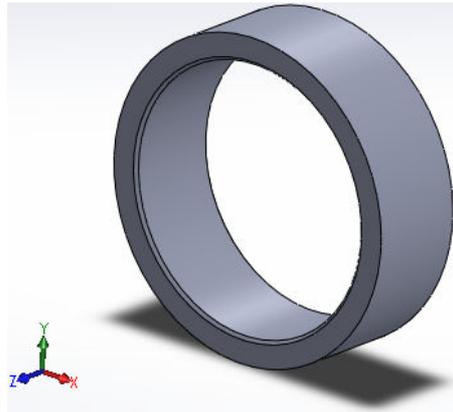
Casquillo que sirve de anclaje axial entre el engranaje y el rodamiento en los árboles.
